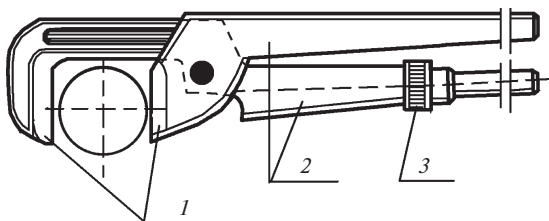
Рычажный трубный ключ «Бако» для отвинчивания контргайек, фланцев, муфт соединительных: 1 — губки зажимные; 2 — ручки-рычаги; 3 — регулятор зажима губок
